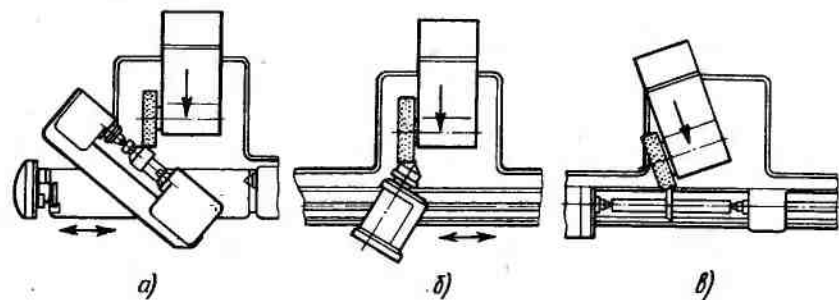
Схема наладки станка для шлифования поверхности с большой конусностью
